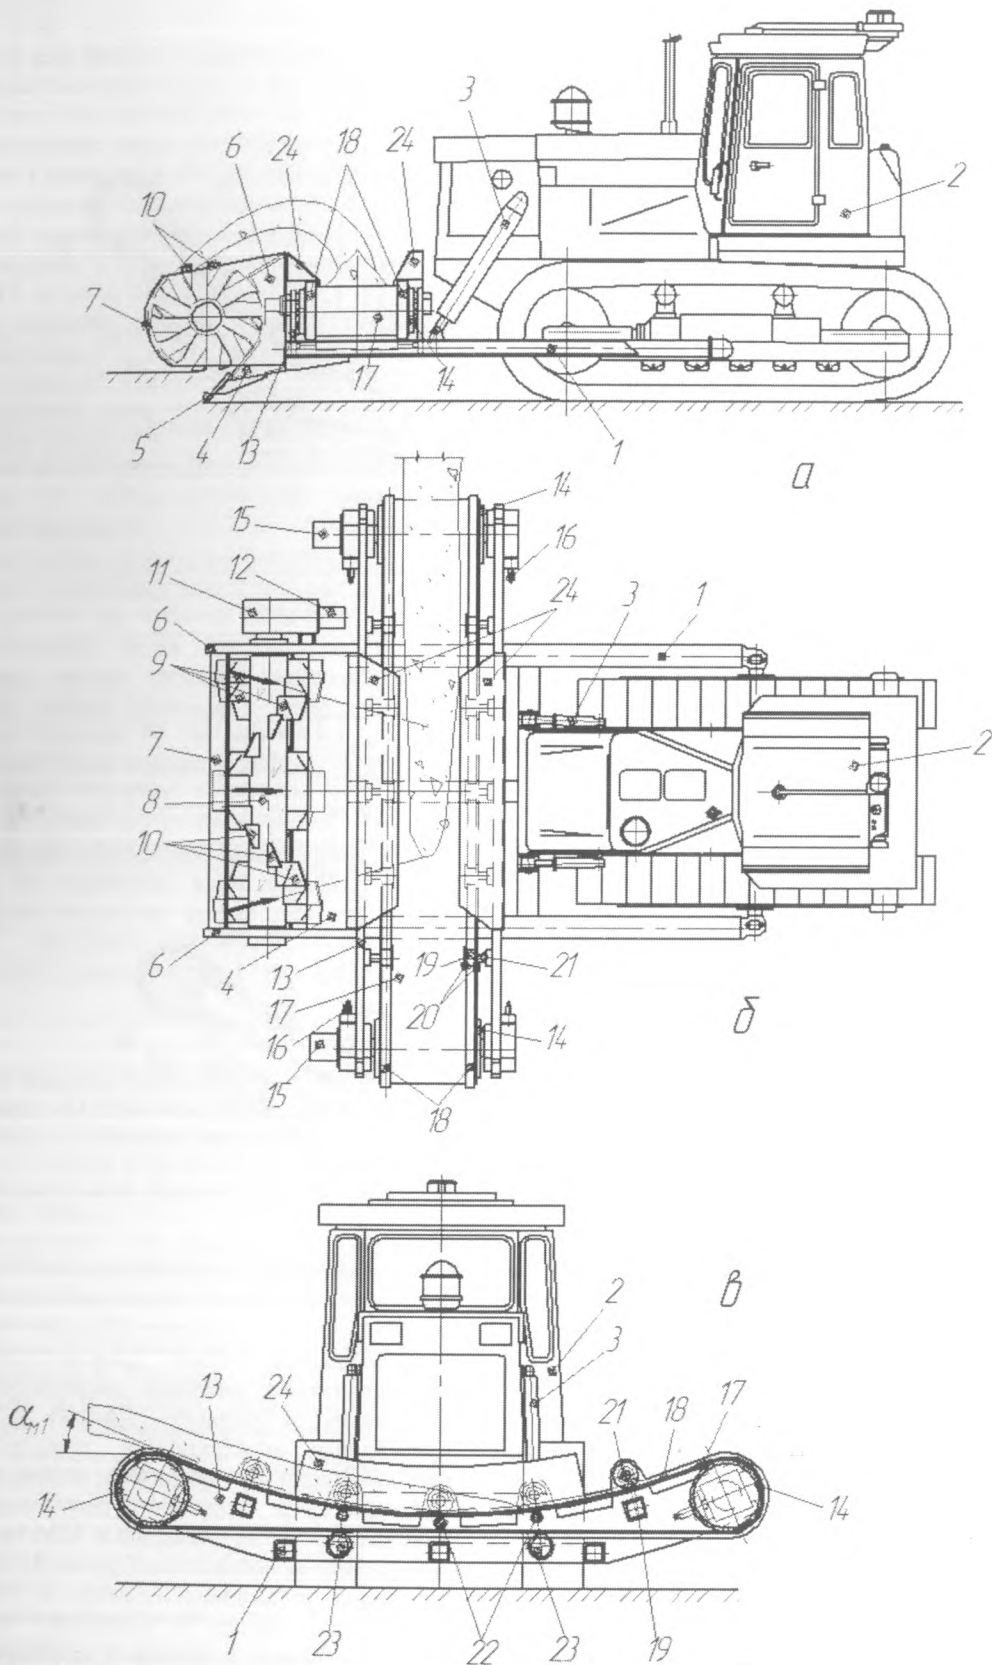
Робоче обладнання землерійно-транспортної машини з використанням різально-металевого робочого органа та конвеєра-металічника для бічного транспортування ґрунту: а-вид збоку; б-вид зверху; в-повздовжній переріз конвеєра-металічника
